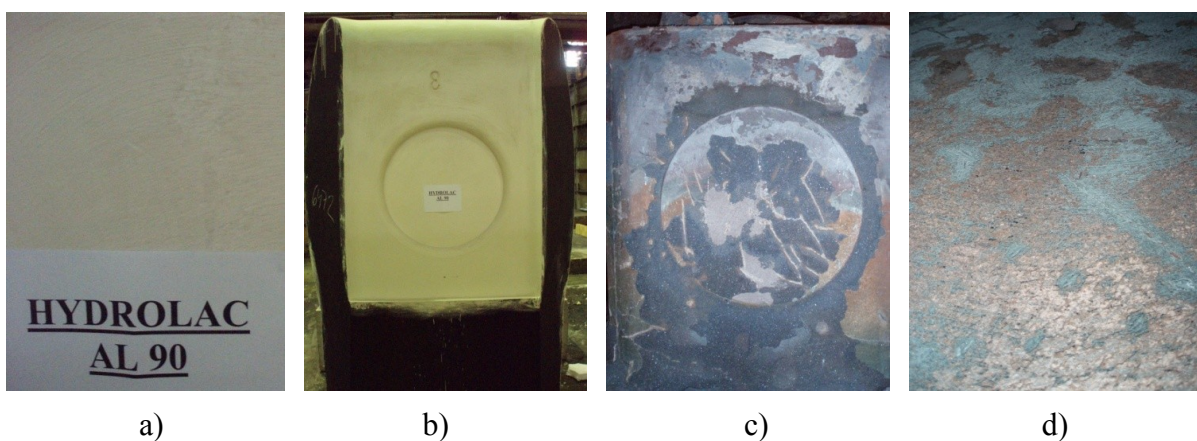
Jádru číslo 1 – a) detail naneseného nátěru, b) detail jádra, c) plocha náboje po odlití, d) detail povrchu odlitku před tryskáním
